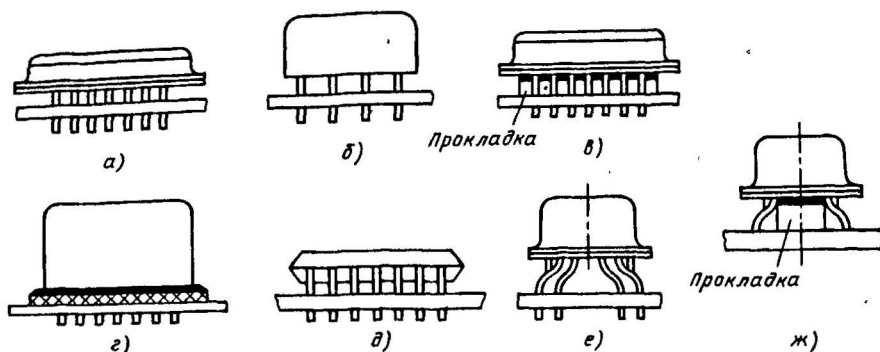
Варианты установки различных корпусов на печатную плату с металлизированными отверстиями
